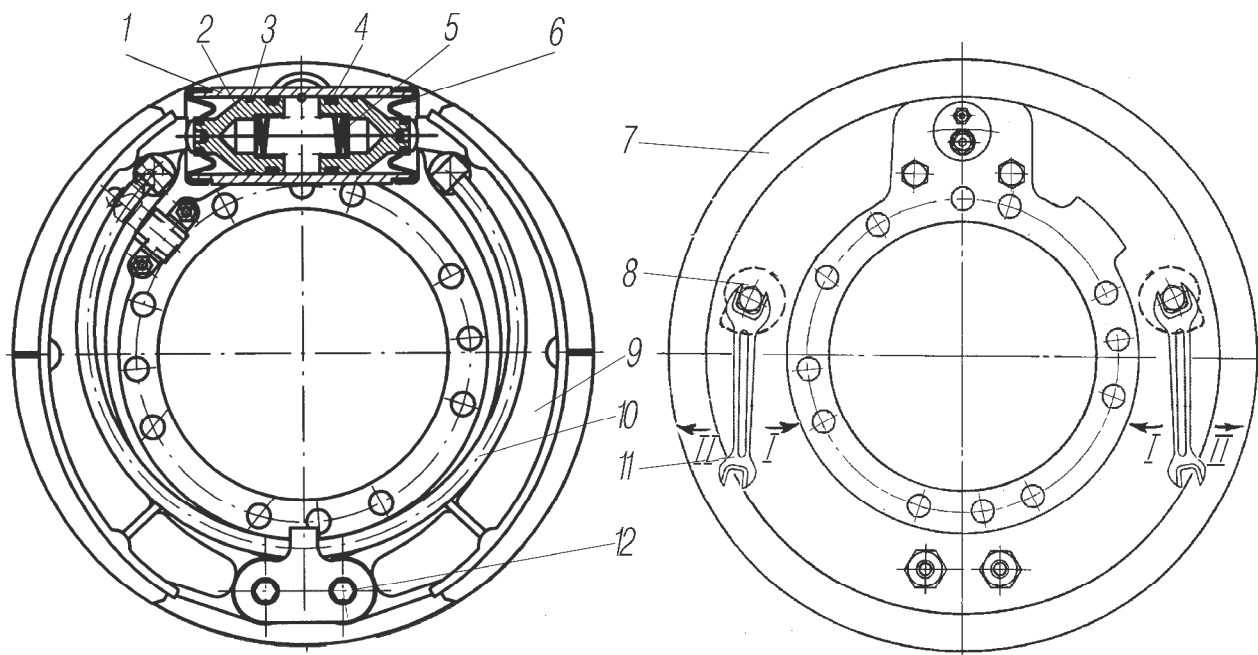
Механизм тормозной рабочий с однополосным цилиндром:
